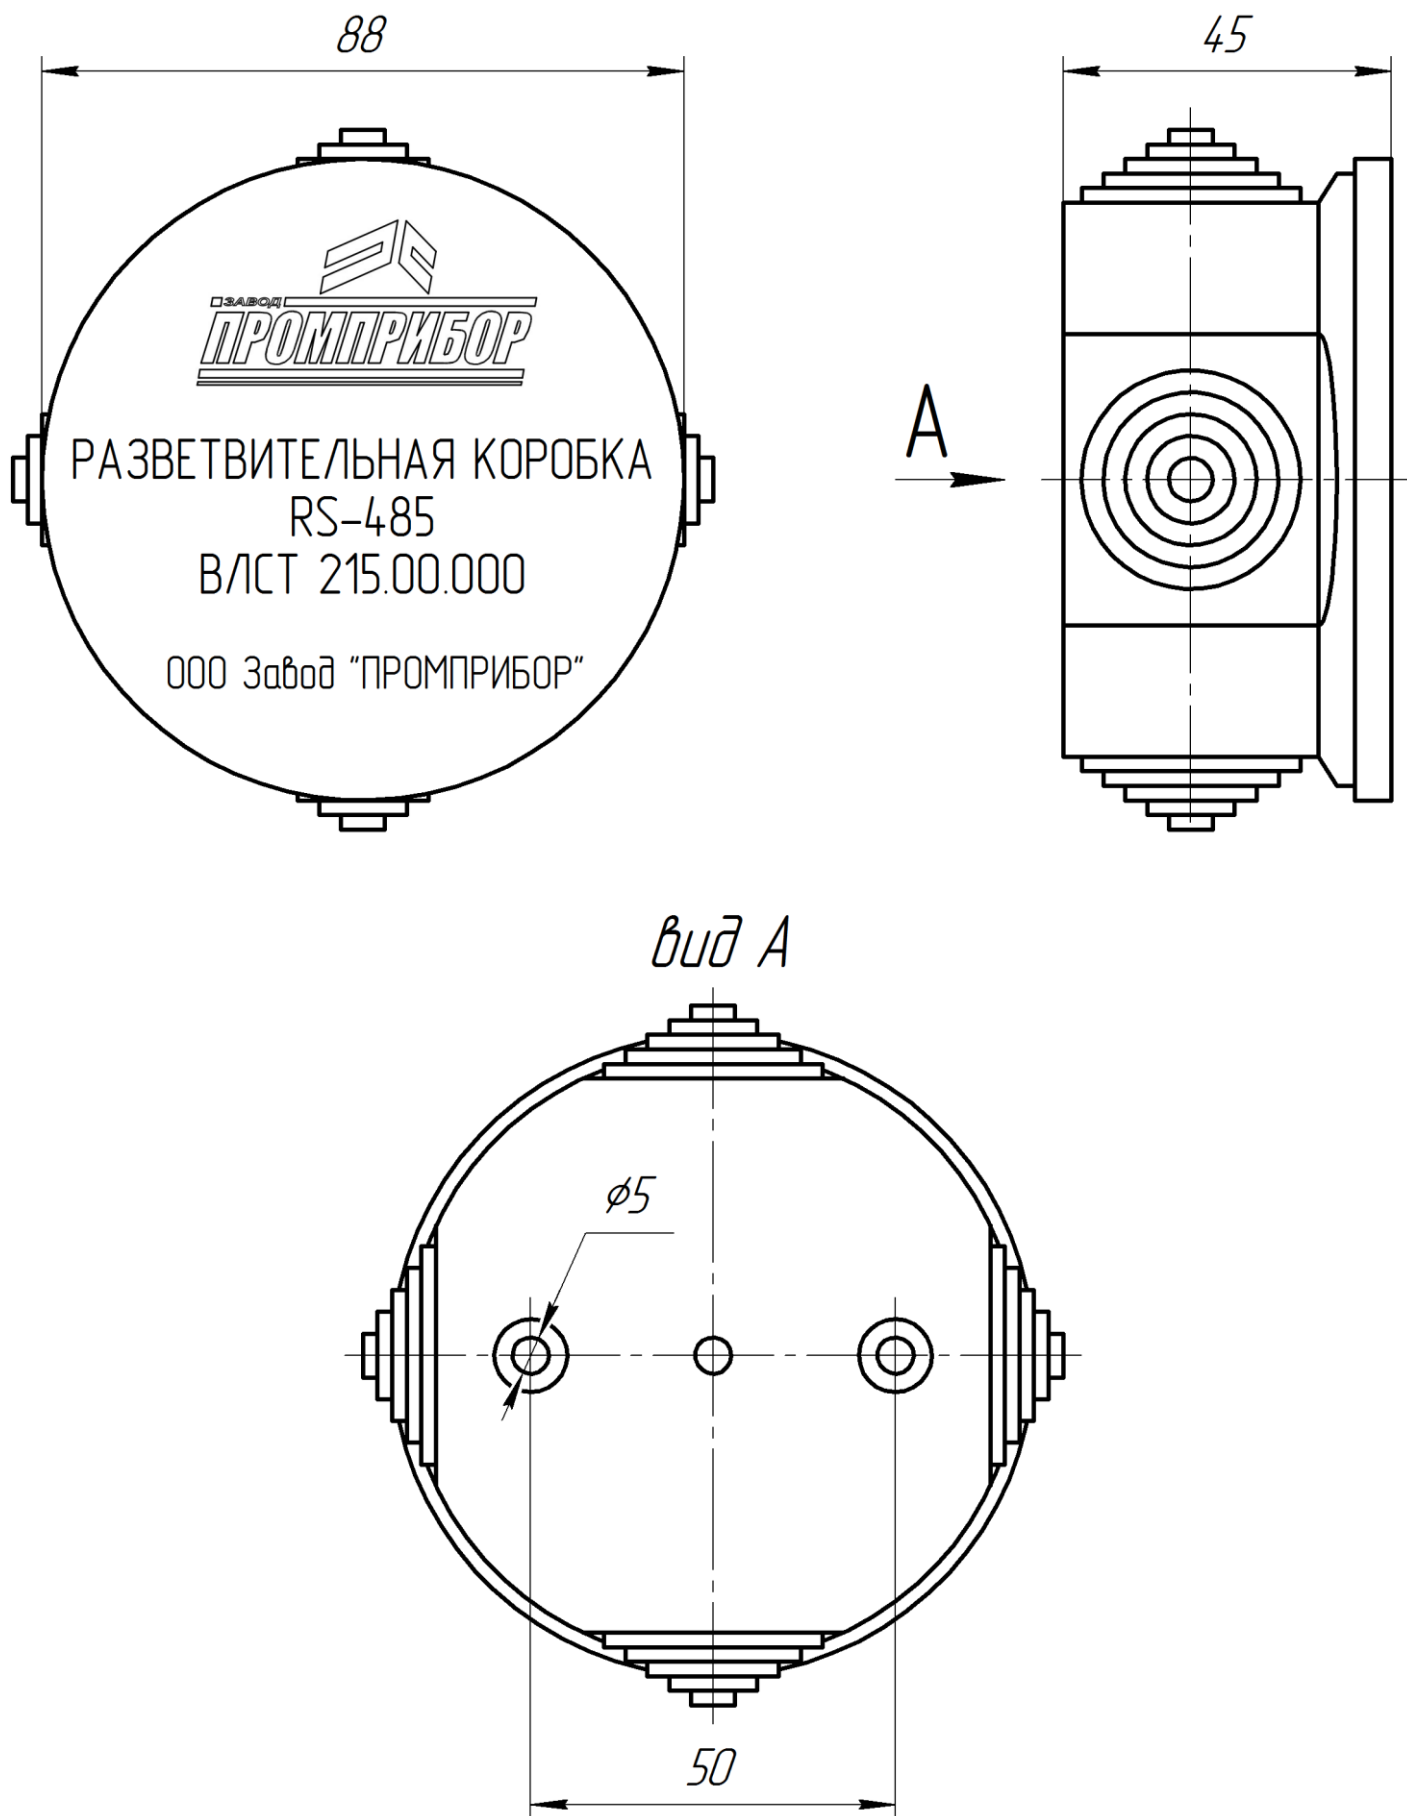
Габаритные и присоединительные размеры разветвительной коробки
